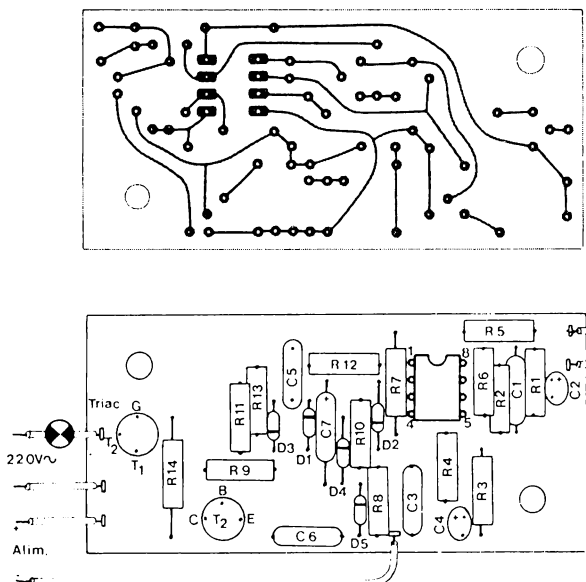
Autre version du circuit imprimé pour le récepteur de la figure 5-7, conçue pour composants de taille réduite. Dimensions : 35 × 75 mm
